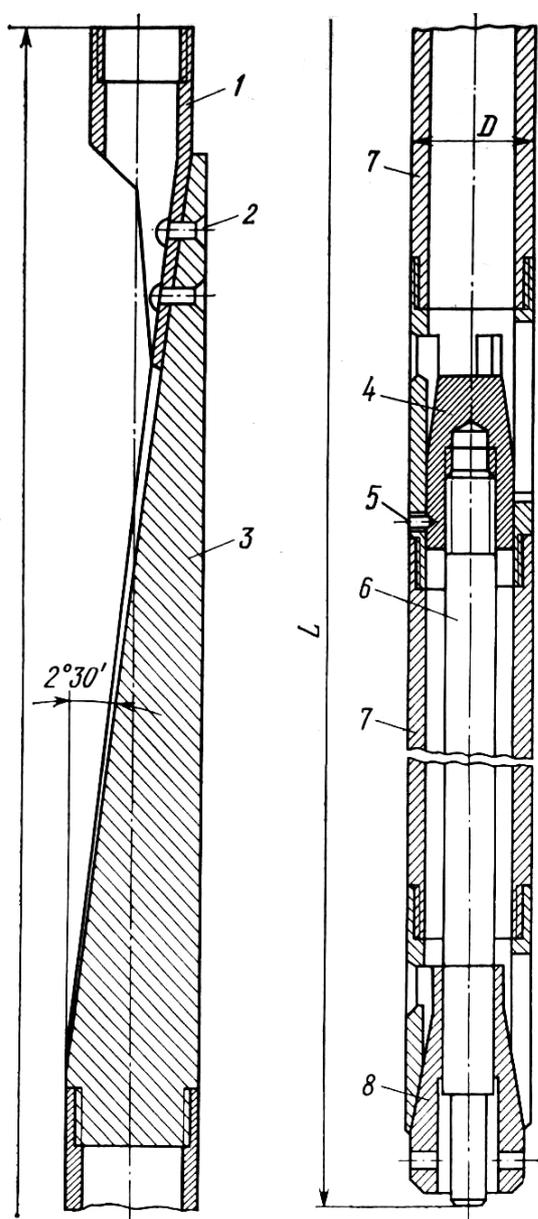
Стаціонарний відхиляючий клин КОС: 1 – установлювальна труба; 2 – заклепки; 3 – клин; 4, 8 – розпірні конуси; 5 – кріпильний гвинт; 6 – шток; 7 – з’єднувальний патрубок
